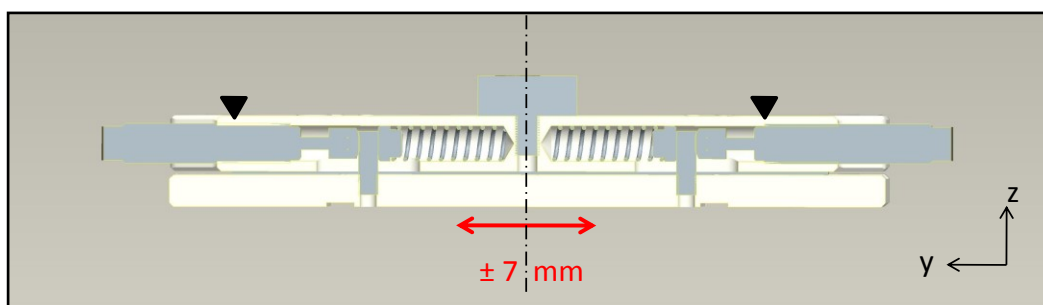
4 - Sistema massa-molla-smorzatore, sezione trasversale, posizione di riposo
